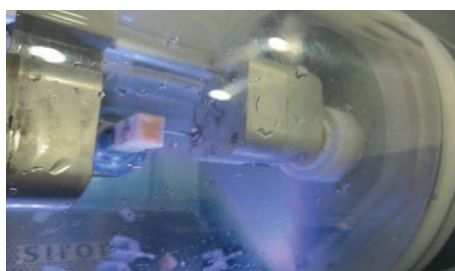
e 11. Colocação e fresagem do bloco selecionado na máquina fresadora.
